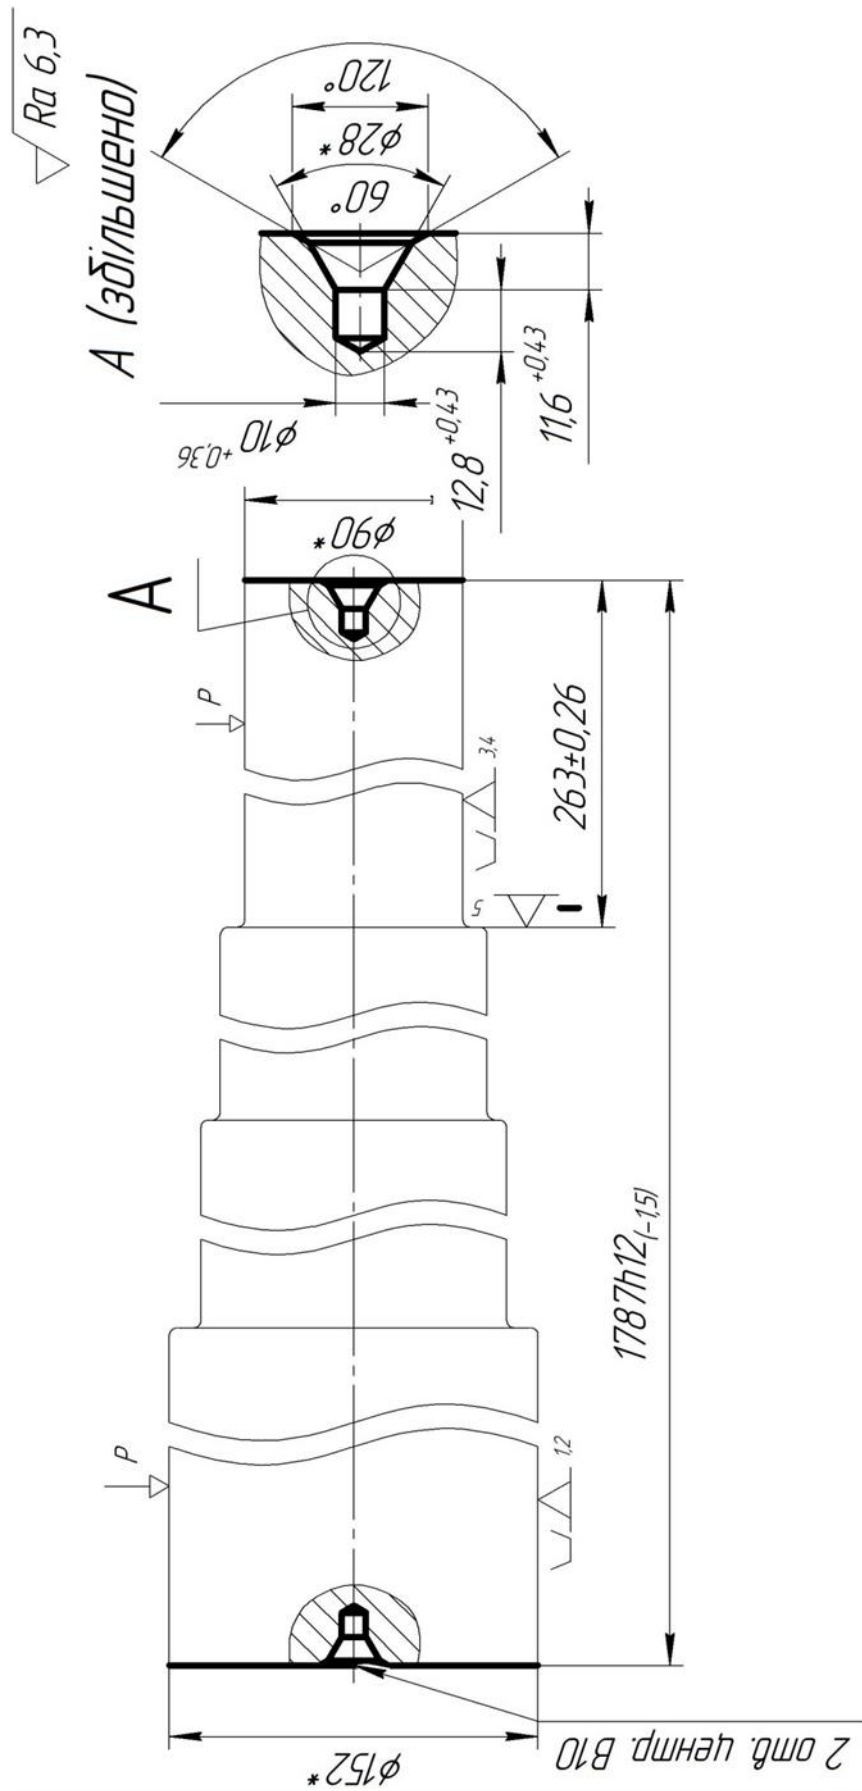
Схема базування і закріплення заготовки на фрезерно-центрувальній операції
